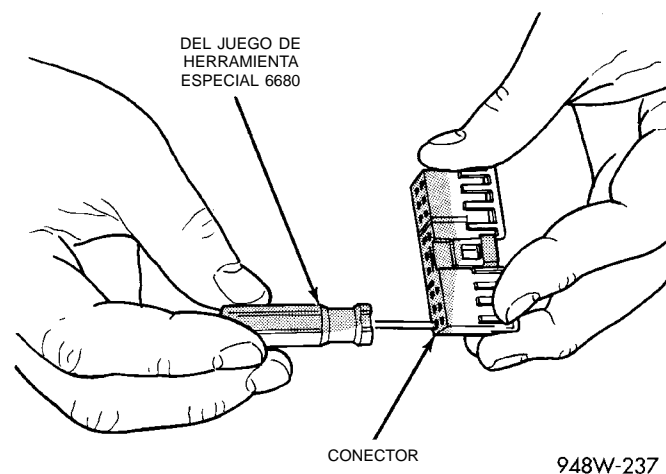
Desmontaje de terminal utilizando la herramienta especial
